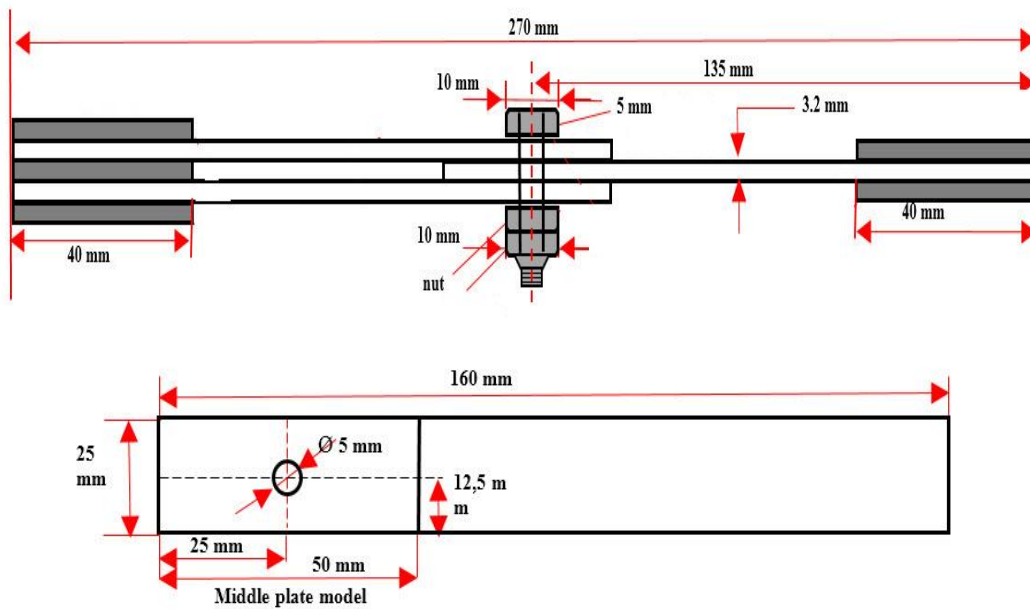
la géométrie d'éprouvette d'aluminium 7075-T6.
